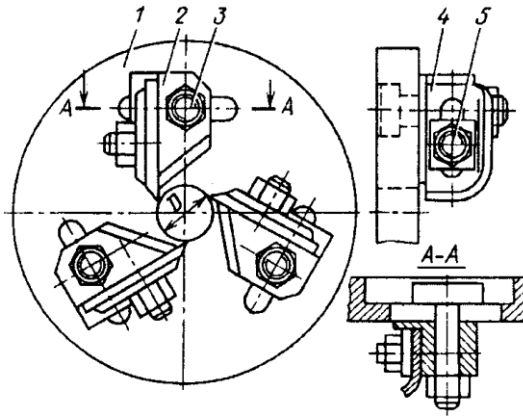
Ножова головка круглопалкового верстата: 1 – корпус; 2 – різцетримачі; 3, 5 – болти; 4 – ніж
